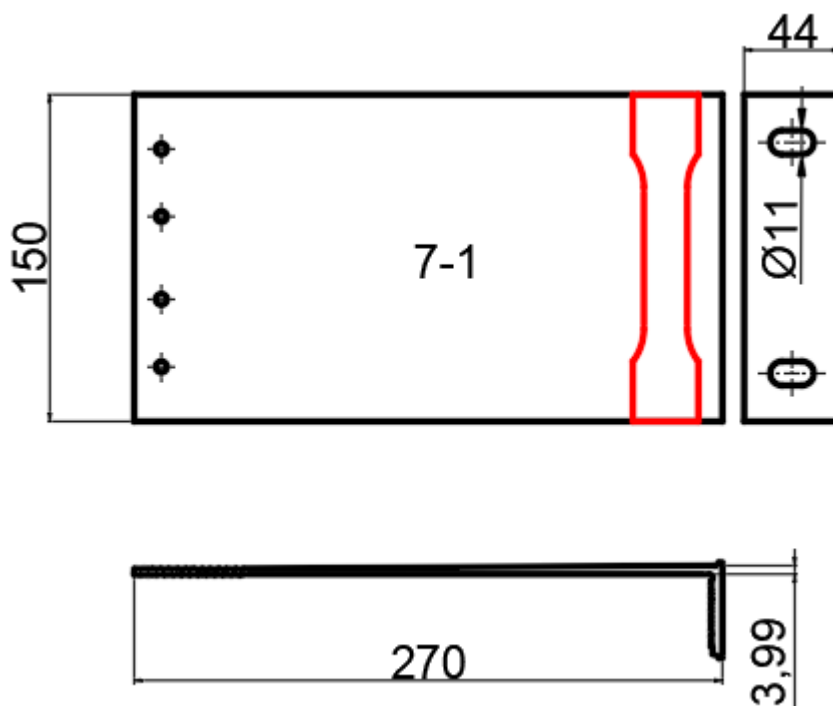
Образцы для испытаний на растяжение. Расположение заготовки
